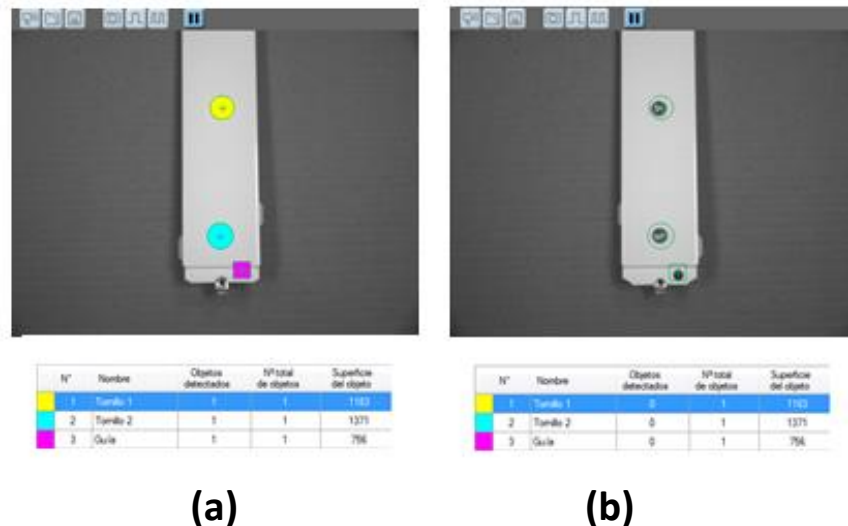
Extremo en el que hay que tapar los tornillos (a) y extremo en el que no hay que tapar los tornillos (b)
